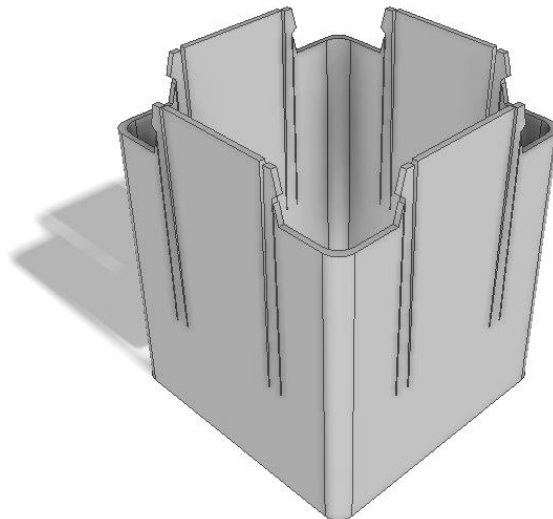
Esempio di Cantilever Beams applicati su di un tubolare a sezione quadra.
